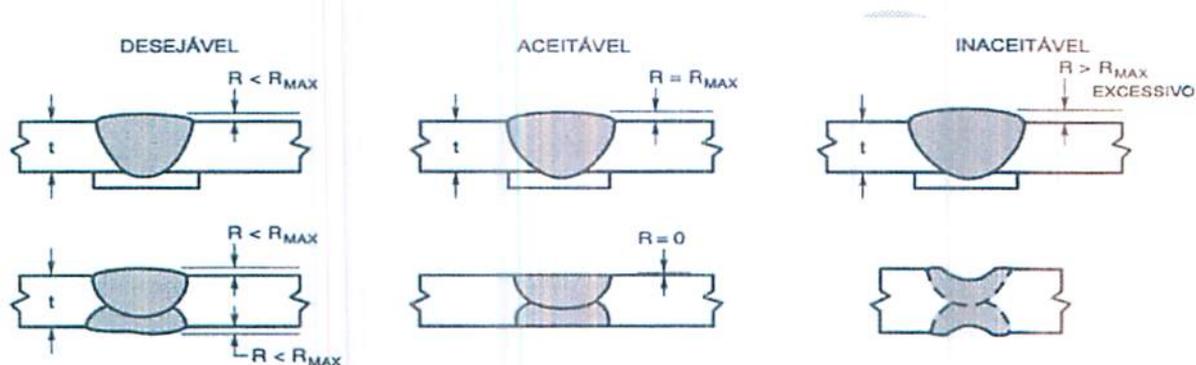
PERFIS DAS SOLDAS EM JUNTA DE TOPO
